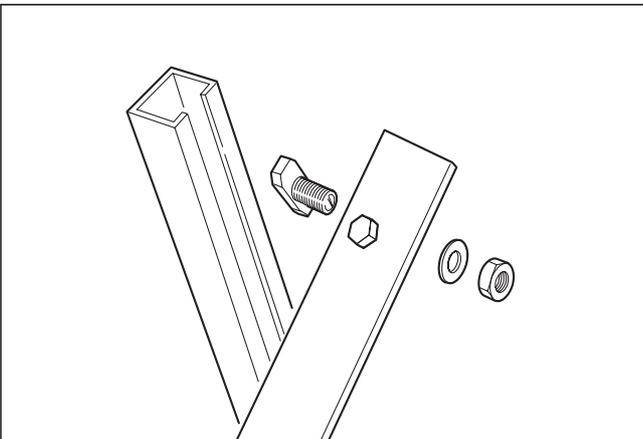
Свободные концы смонтированных профилей С соединить болтами с квадратной головкой М10х30 шайбой и гайкой. Установочный угол выставить согласно таблицы 3.1 и, при необходимости спилить выступающий конец профиля С.
